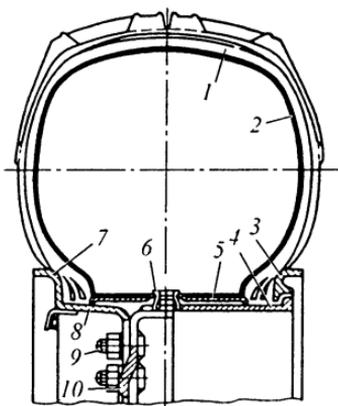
Шина с регулируемым давлением воздуха: 1 — покрышка; 2 — камера; 3 — бортовое кольцо; 4 — внутренняя часть обода; 5 — распорное кольцо; 6 — направляющая вентиля камеры; 7 — закраина обода; 8 — наружная часть обода; 9 — шпилька крепления обода; 10 — диск колеса
